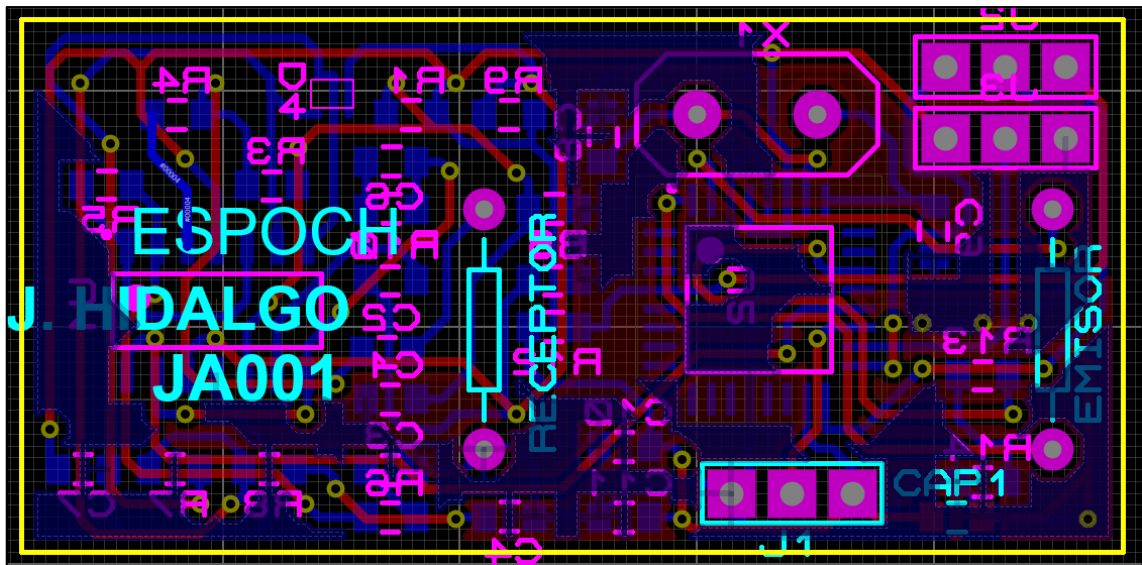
Diseño del PCB para el primer prototipo de sensor inteligente.
